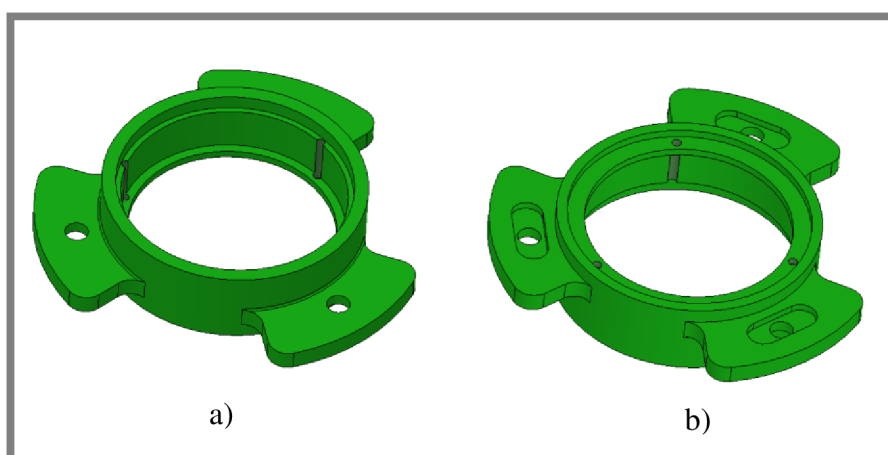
Uchycení vnitřního kroužku ložiska a) spodní disk, b) horní disk
